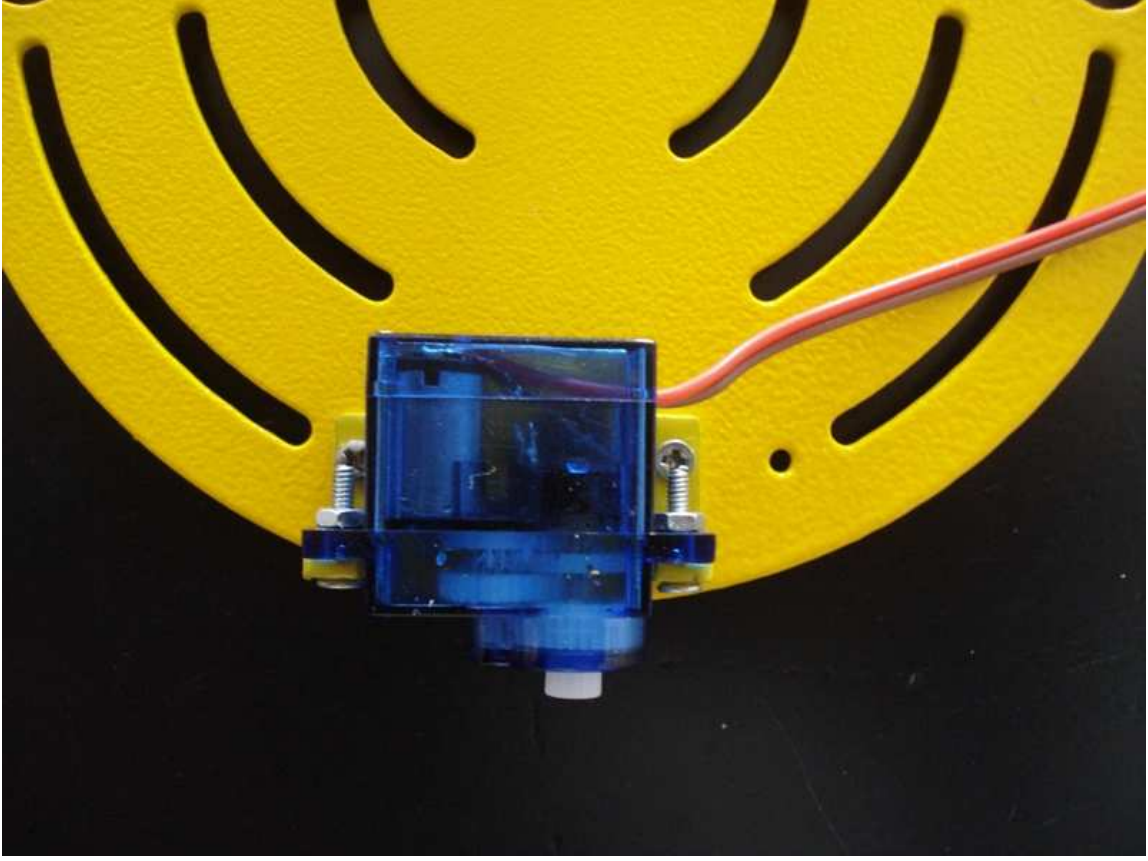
Servo motor ile L montaj parçalarının bağlantıları.
